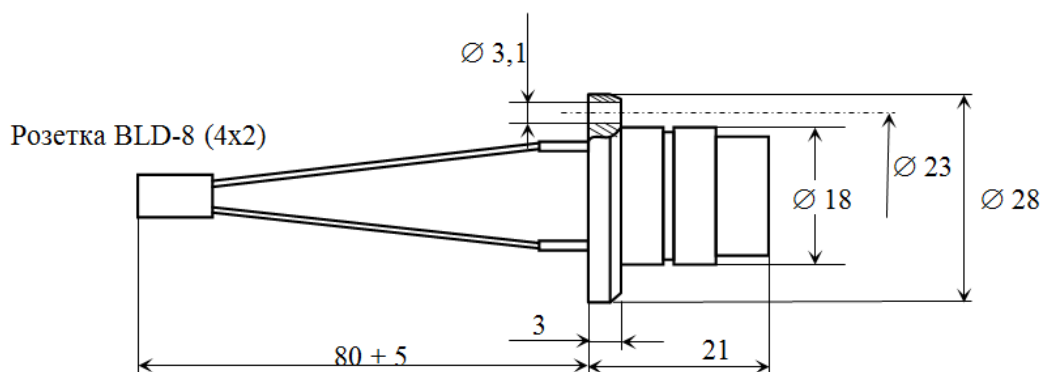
Внешний вид и габаритные размеры УФРО2
